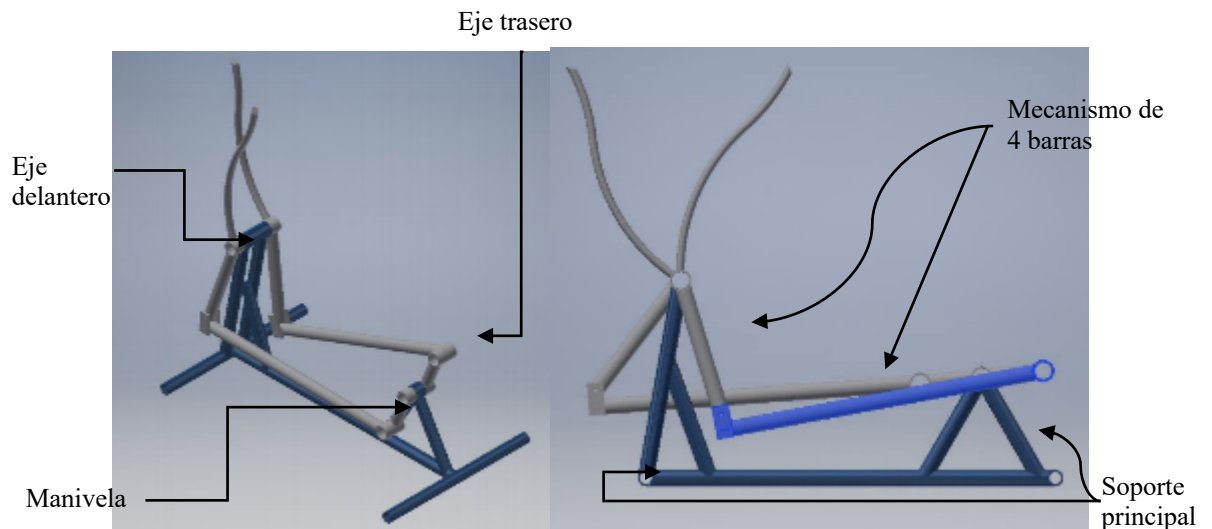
Vista isométrica de máquina elíptica diseño preliminar (Izquierda); Vista lateral de máquina elíptica diseño preliminar (Derecha).
